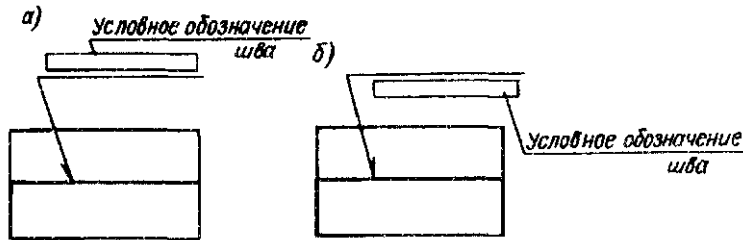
Нанесение обозначения сварного шва: а — шов на лицевой стороне; б — шов на оборотной стороне
